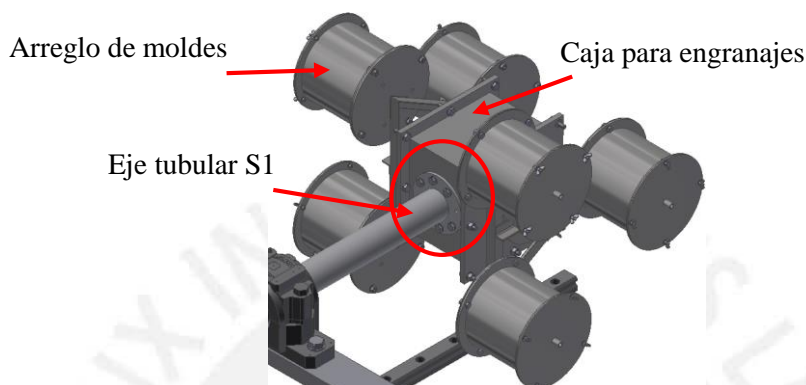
Unión atornillada del eje tubular S1 a la caja para engranajes.
